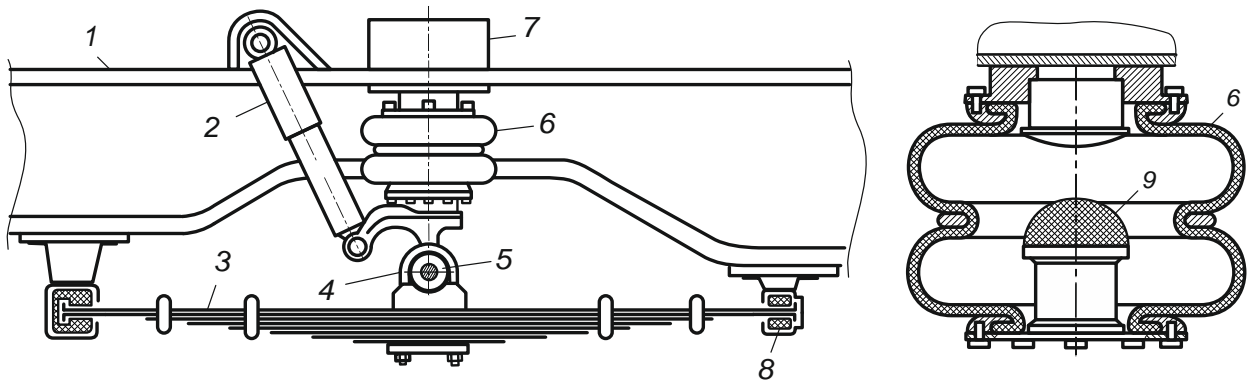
Принципиальная схема рессорно-пневматической подвески автомобиля:
